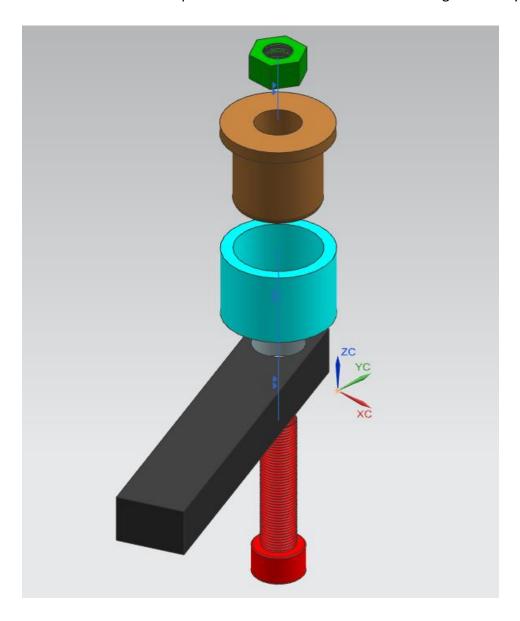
Ensamble del diseño dos (vista isométrico).
